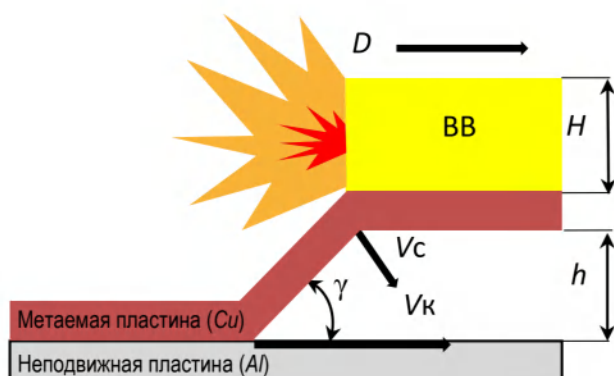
Схема соударения пластин при сварке взрывом: ВВ – взрывчатое вещество (аммонит 6 ЖВ+песок); D – скорость детонации; V_c – скорость точки контакта; V_k – скорость соударения; γ – угол соударения; H – высота заряда; h – высота зазора
